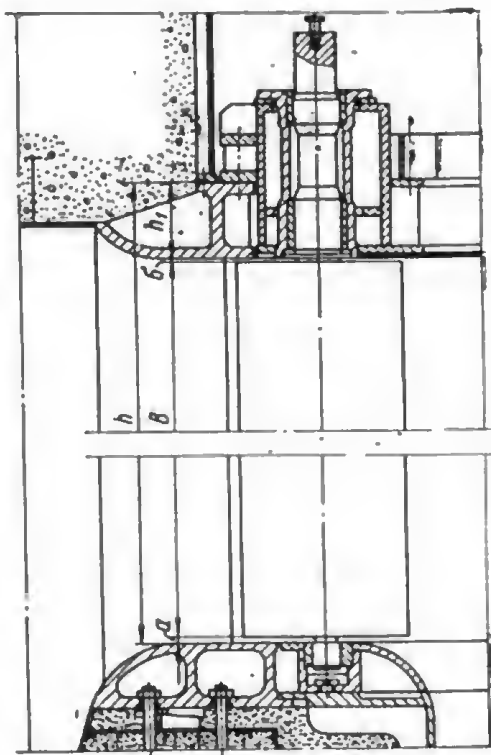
Схема проверки высоты направляющего аппарата.
